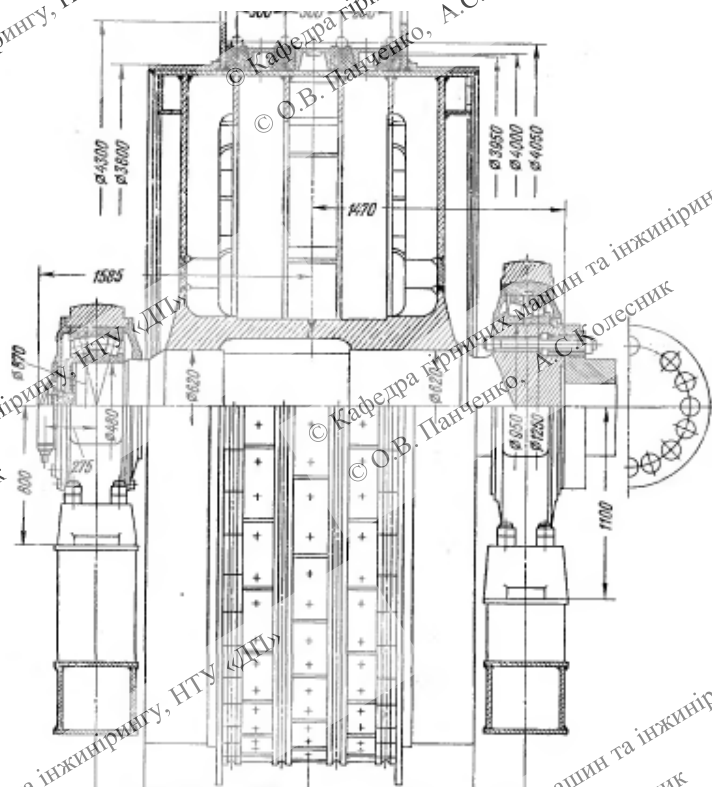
Збірка головного валу баштованої машини МК 4×4Р, з редукторним приводом [2]
